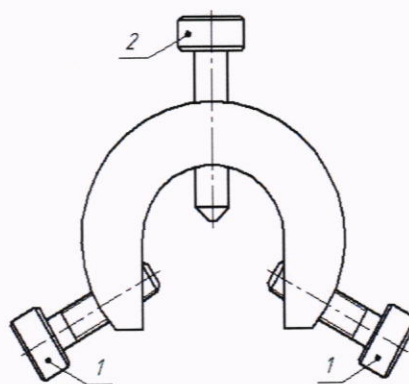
приспособление для проверки уровнемеров с коаксиальным зондом:
